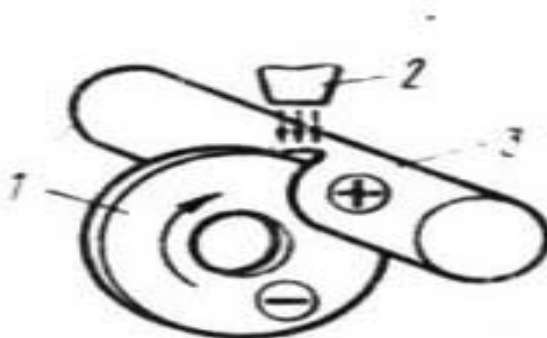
Схема анодно-механической обработки диском: 1 –диск инструмент; 2- сопло для подачи электролита; 3 – заготовка.
